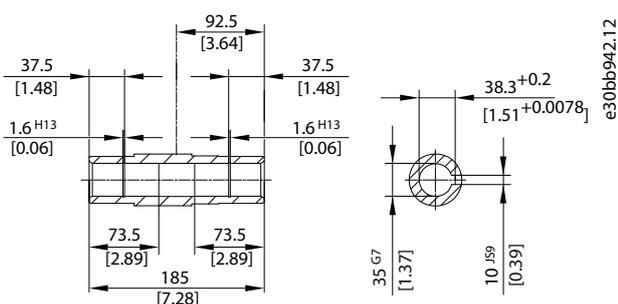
Вал 35 мм из стали/нержавеющей стали
